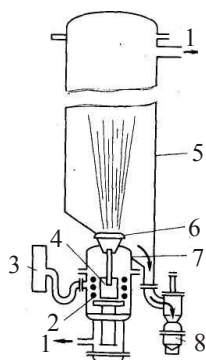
Схема установки для вакуумного розпошення розплавлених металів: 1 — відвід до вакуумному насоса; 2 — індуктор; 3 — генератор для живлення індуктора; 4 — тигель з розплавом алюмінію; 5 — камера розпошення; 6 — затвор; 7 — камера плавлення; 8 — контейнер для порошку
